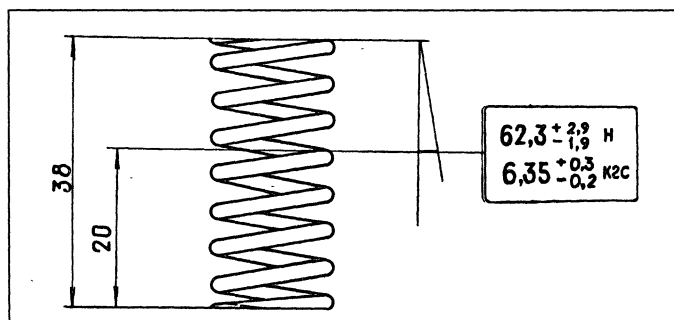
Основные данные для проверки пружины редукционного клапана
